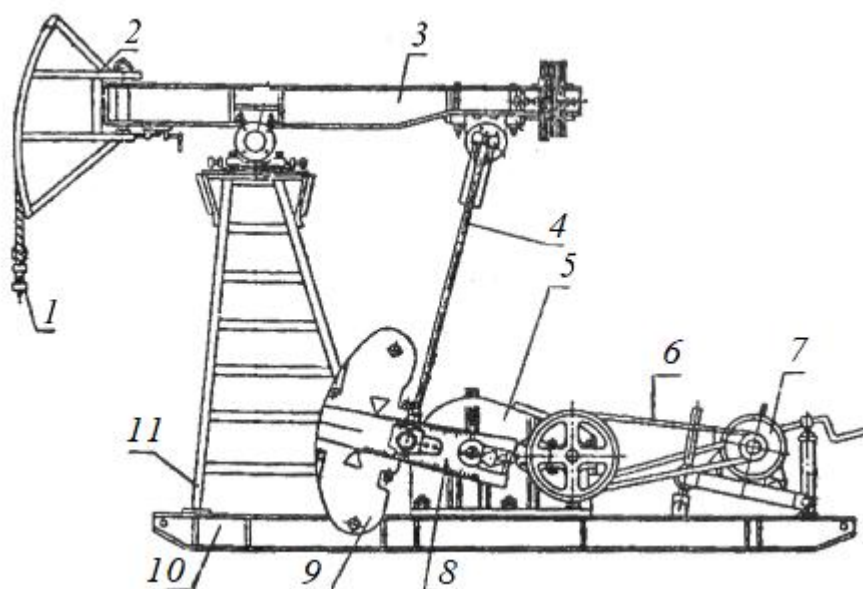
Конструктивная схема баланси́рного станка-качалки:
